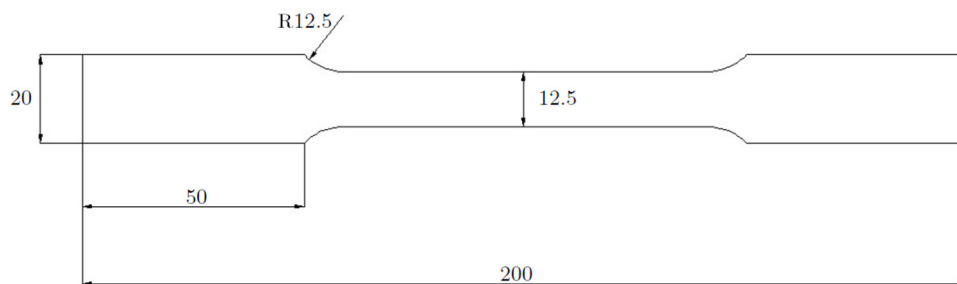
Dimensiones de las probetas de tracción uniaxial.
